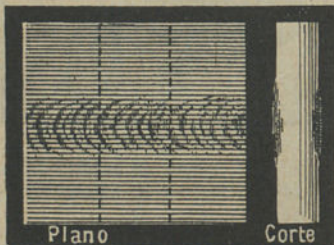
Fraccionamento duma soldadura para ensaios de dobra.
